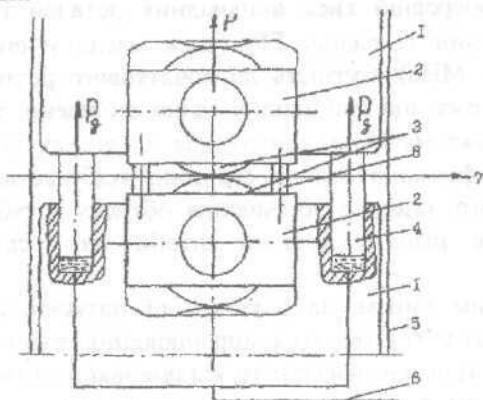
Схема попереднього розтягування кліті гідродомкратами: 1 – подушки опорних валків; 2 – подушки робочих валків; 3 – робочі валки; 4 – гідродомкрати; 5 – стійки станини; 6 – магістраль подачі масла; 7 – штаба; 8 – плунжери урівноваження верхнього робочого валка
